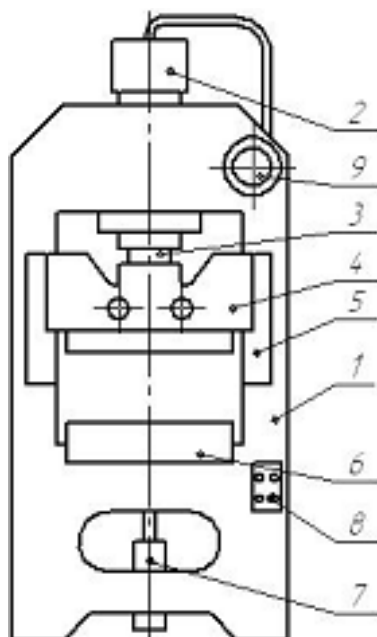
Схема пресса рамной конструкции: 1 – сварная рама; 2 – главный гидроцилиндр двойного действия; 3 – плунжер; 4 – ползун; 5 – направляющая; 6 – стол; 7 – гидроцилиндр выталкиватель; 8 – пульт управления; 9 – манометр
